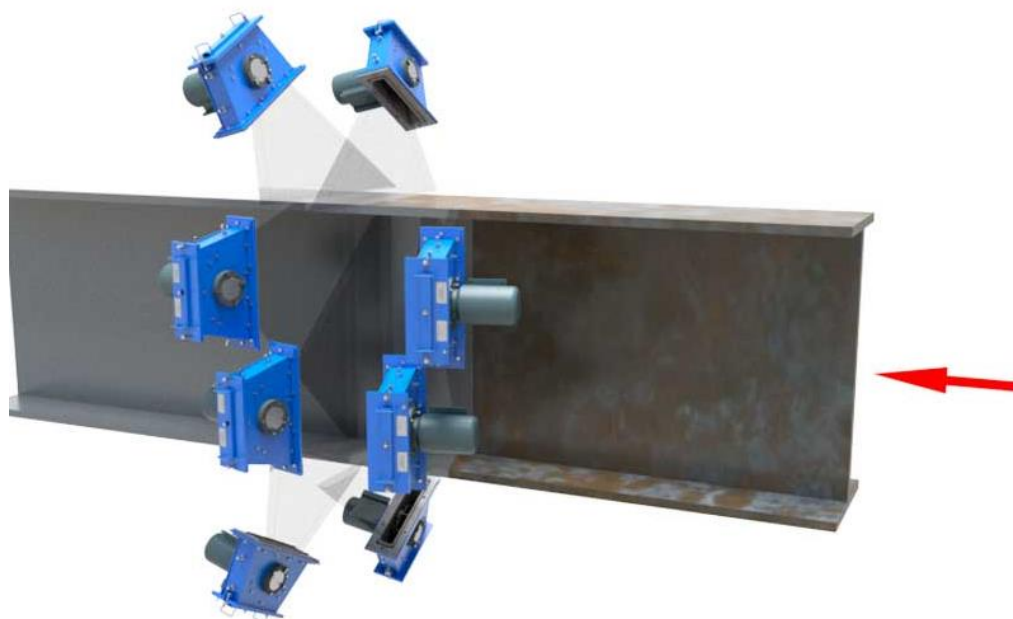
Дробометна камера для очищення зварних металоконструкцій
